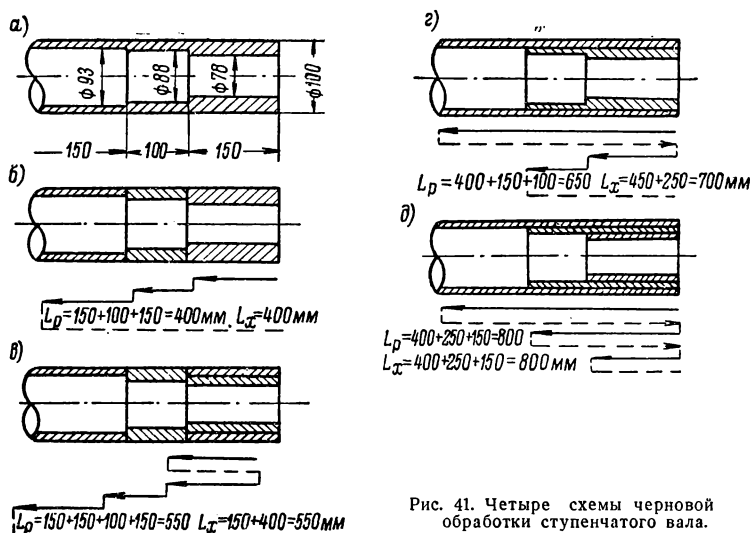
Четыре схемы черновой обработки ступенчатого вала.
